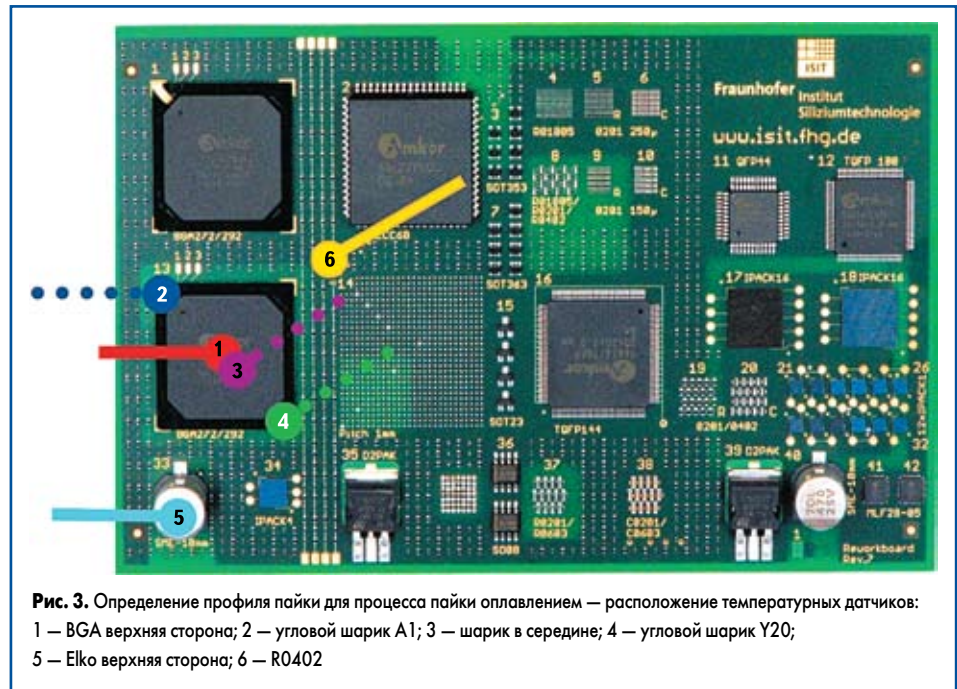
Определение профиля пайки для процесса пайки оплавлением — расположение температурных датчиков: 1 — BGA верхняя сторона; 2 — угловой шарик A1; 3 — шарик в середине; 4 — угловой шарик Y20; 5 — Елко верхняя сторона; 6 — R0402
